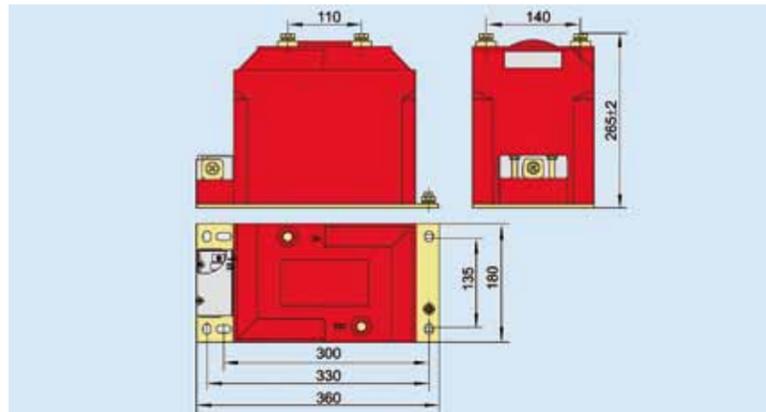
Внешний вид и монтажные размеры трансформатора напряжения JDZ10-10B
